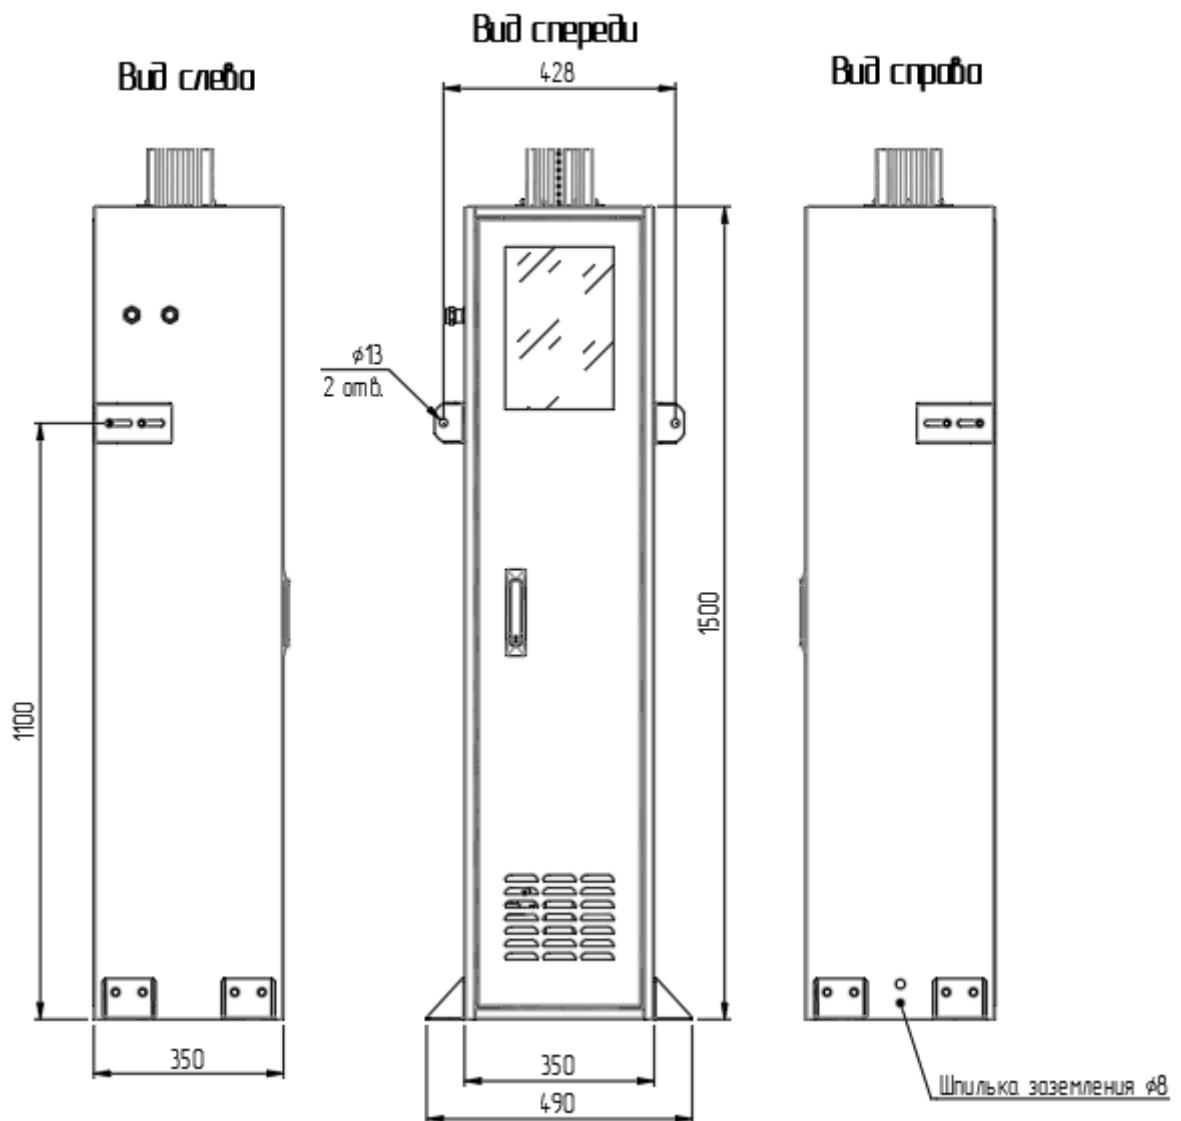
Шкаф ТШВ-1533Н1. Чертеж общего вида.
